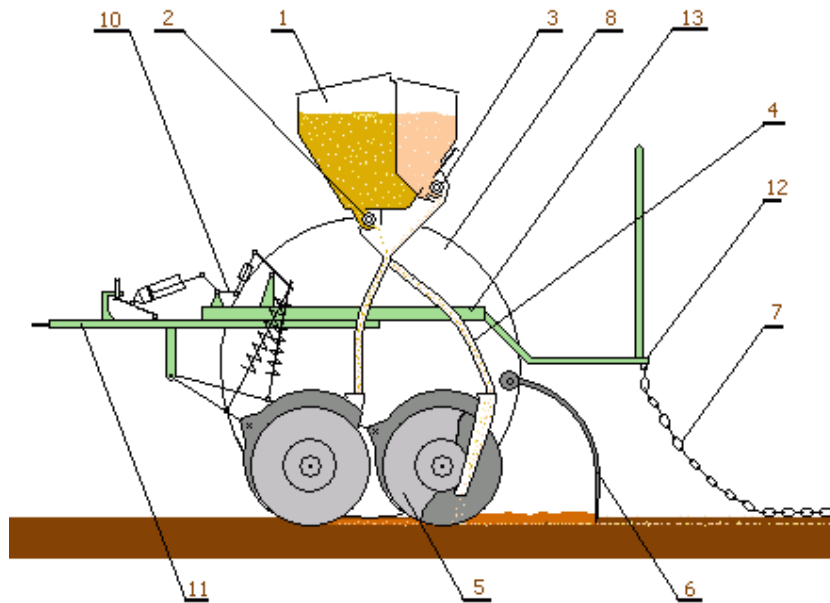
Сівалка зернотукова СЗ - 3,6
